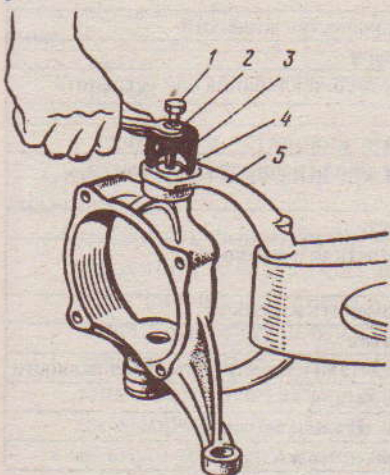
Съемник для выпрессовки втулок рычагов подвески: 1 - распорная втулка захватных лапок; 2 - внутренняя втулка; 3 - захватная лапка; 4 - наружная втулка; 5 - корпус; 6 - крышка корпуса; 7 - шайба; 8 - гайка; 9 - винт; 10 - шайба; 11 - шплинт; 12 - палец
